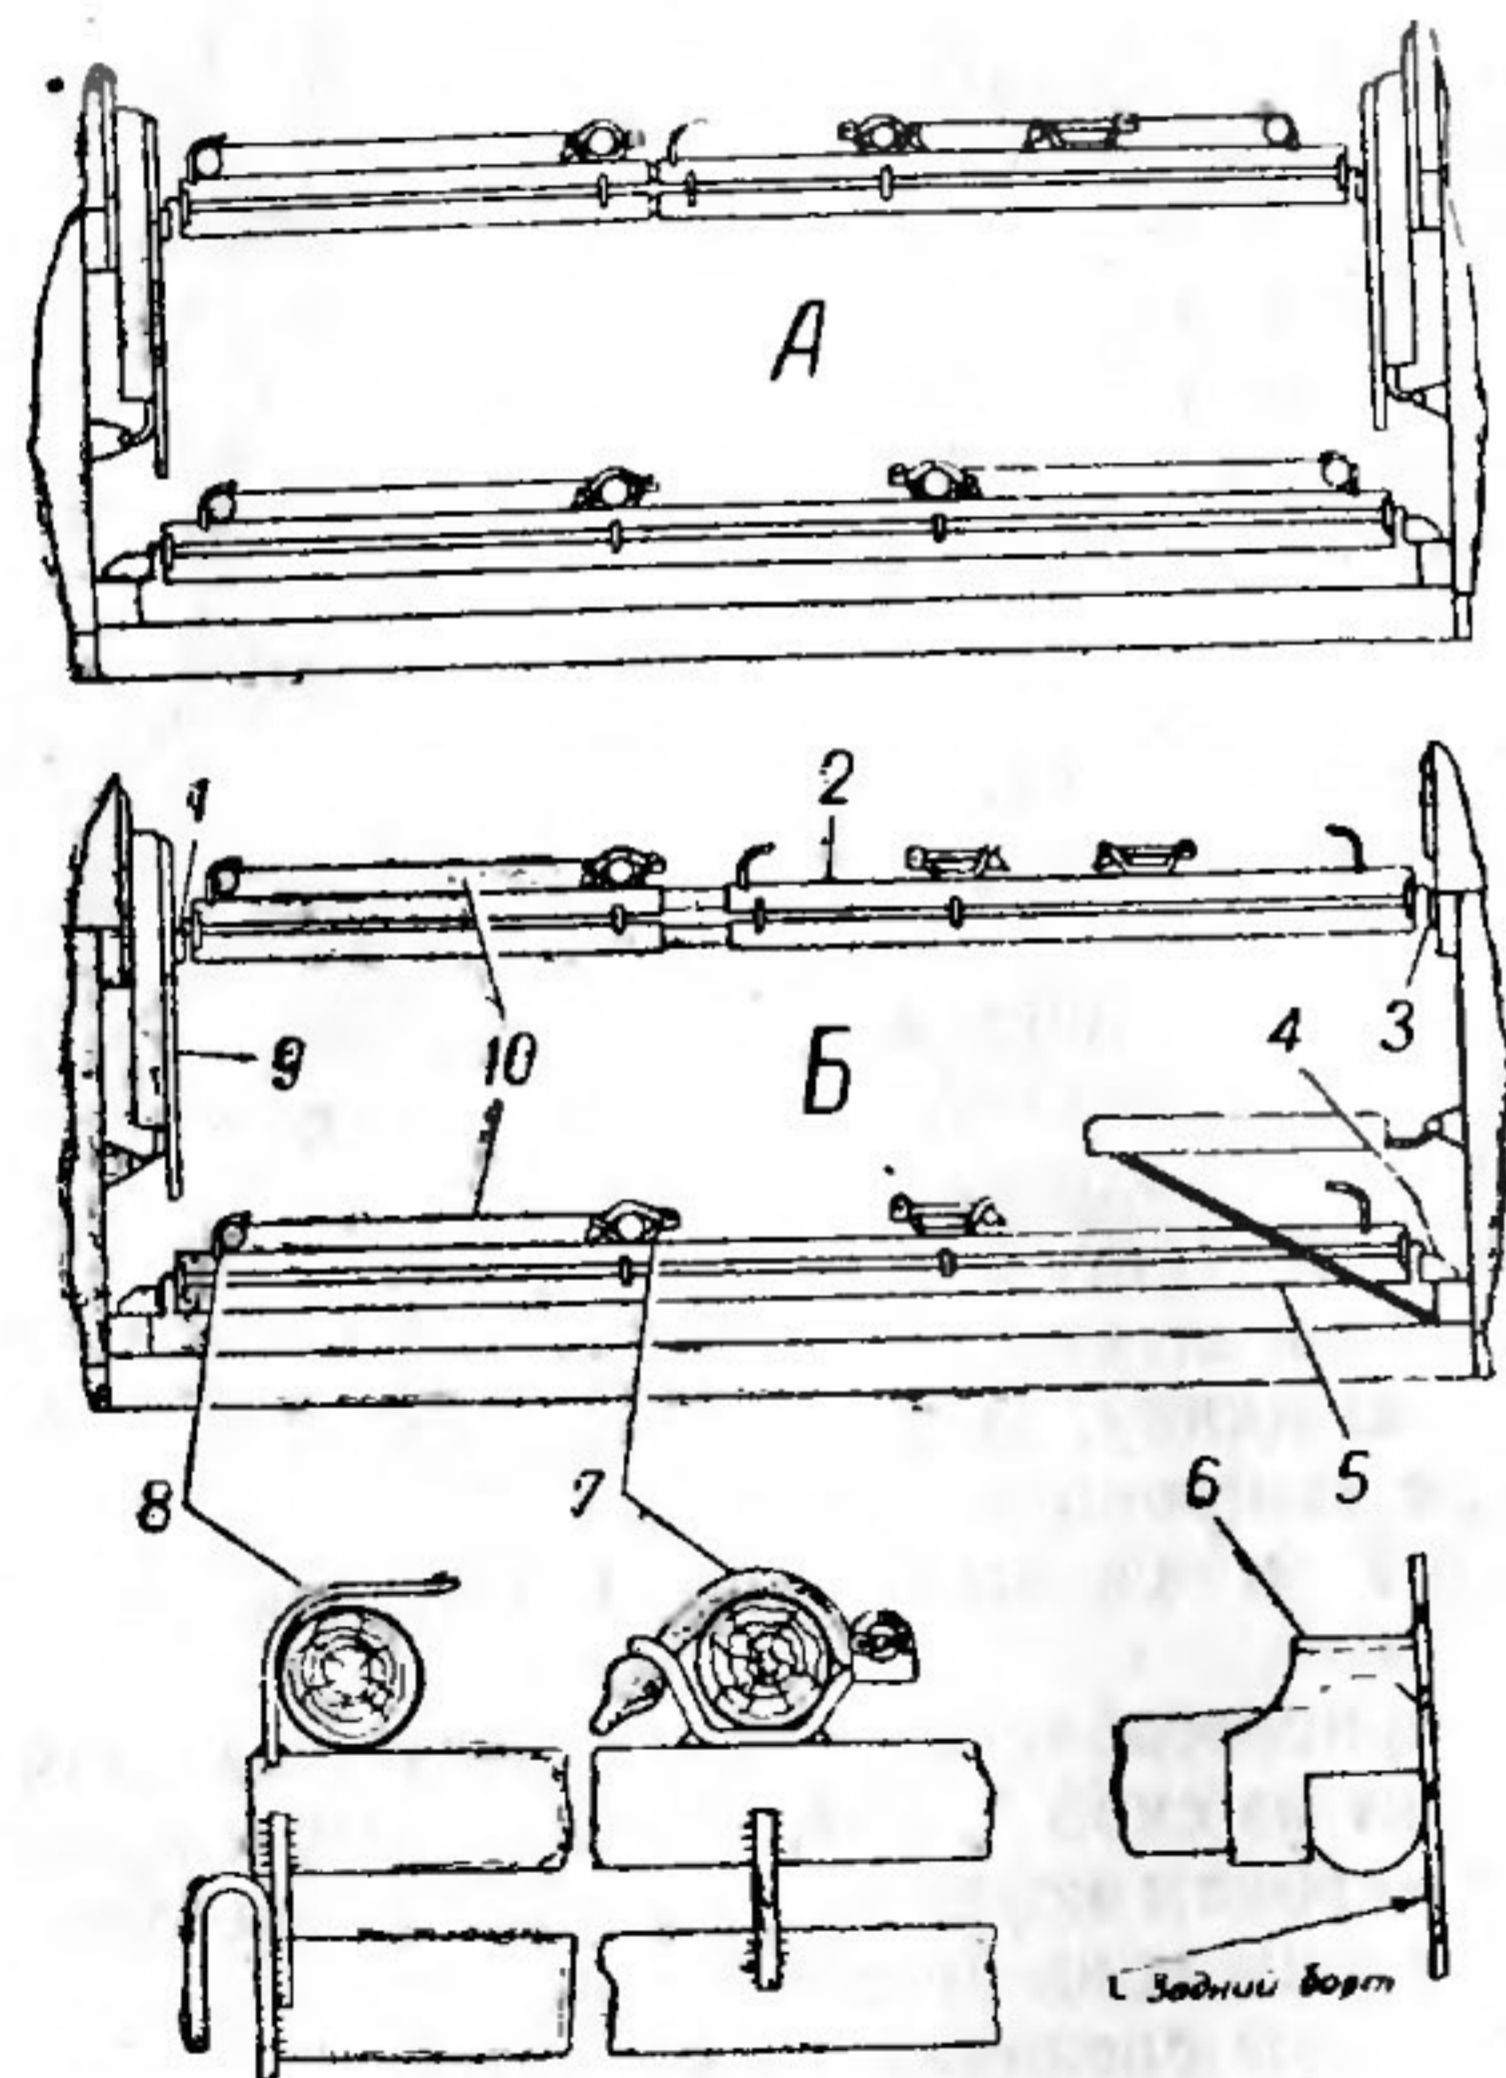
Схемы размещения и крепления санитарных носилок (основные варианты):
